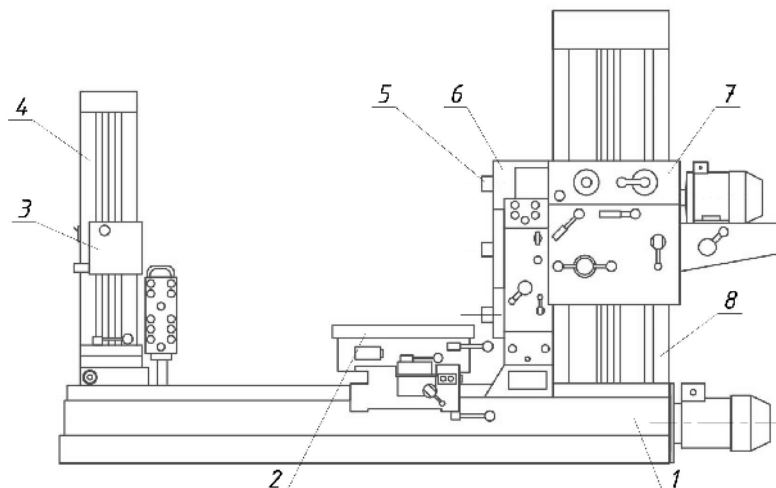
Загальний вигляд горизонтально-розточувального верстата
